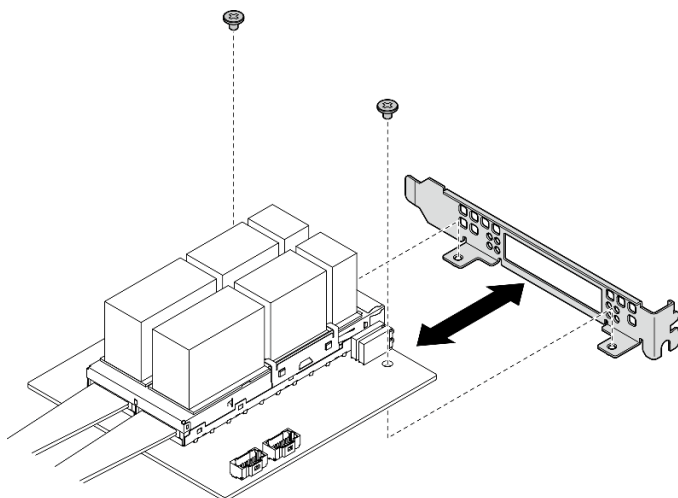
Desensamblaje de la Tarjeta de puerto OSFP
